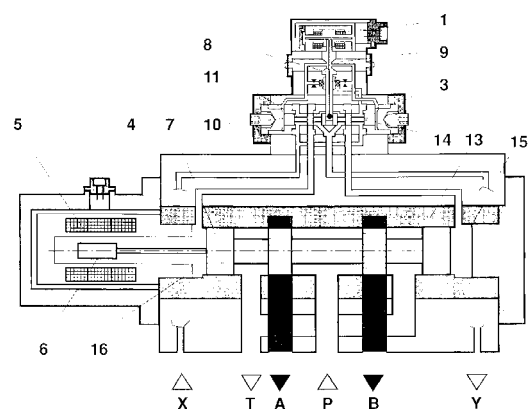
Przykład konstrukcji serwowaworu rozdzielającego z mechanicznym sprzężeniem zwrotnym.[3]
